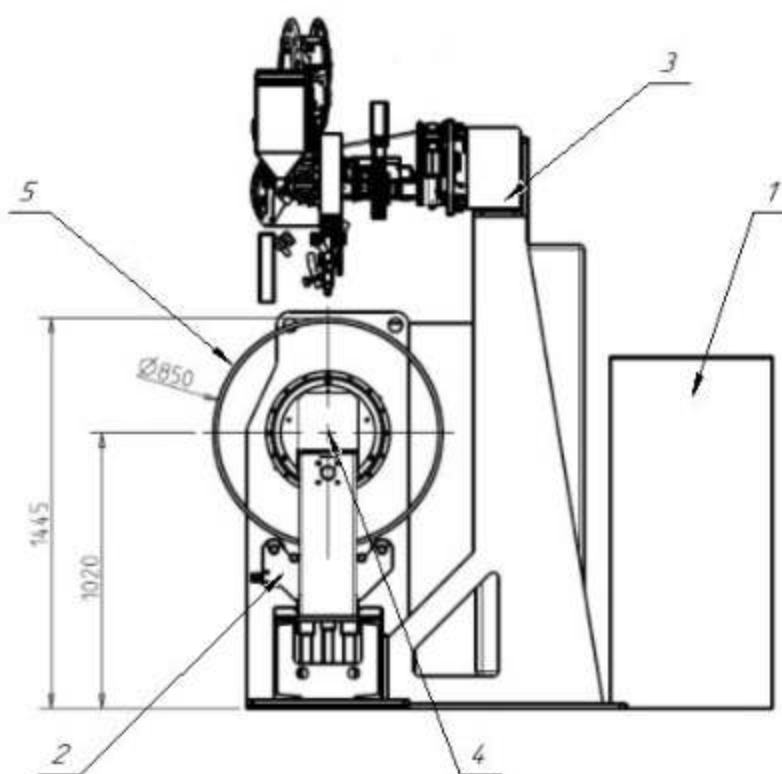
Установка для автоматической сварки кольцевых стыков обечаек корпуса защитного кожуха
